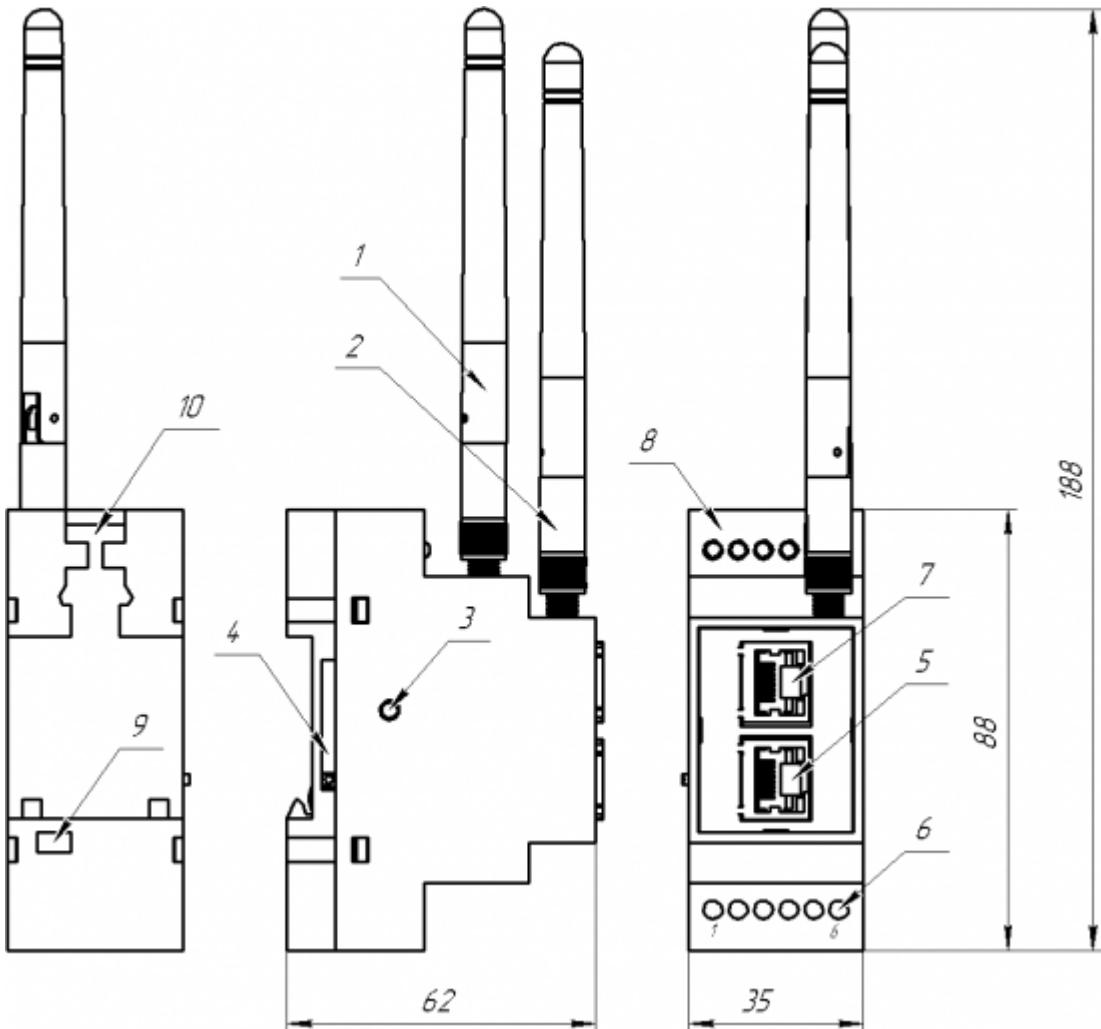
Габаритные размеры и позиционные обозначения СК-01
